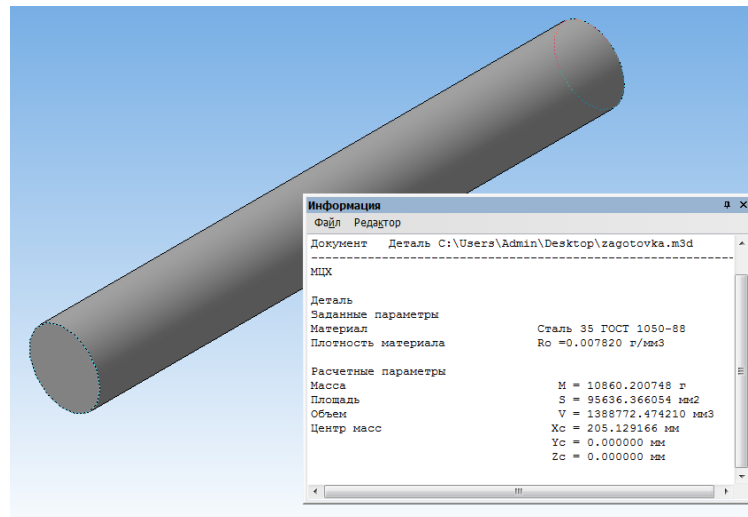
Модель та розрахунок прокату для заготовки «Гвинт опори»
